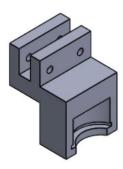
Gripper Diseñado en SOLIDWORKS para Bebidas Embotelladas.
